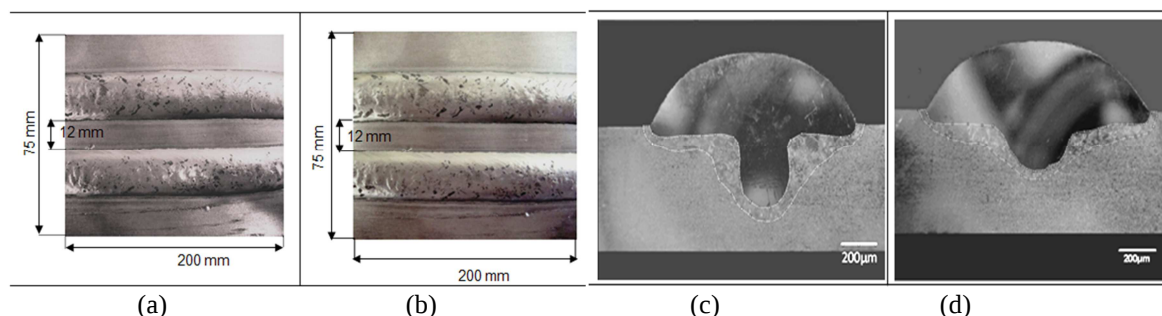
Placas soldadas (a) e (b) e perfis do cordão de solda resultantes (c) e (d); (a) e (c) puxando; (b) e (d) empurrando
